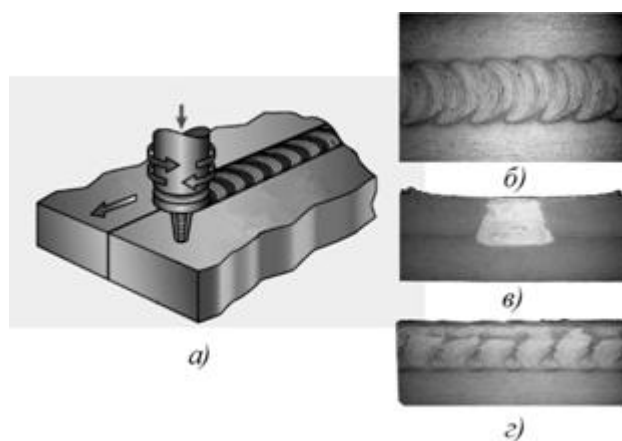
ПСТ с возвратно-вращательным движением инструмента: а – схема сварки; б – вид сварного шва; в – сечение перпендикулярное направлению шва; г – сечение вдоль шва.
